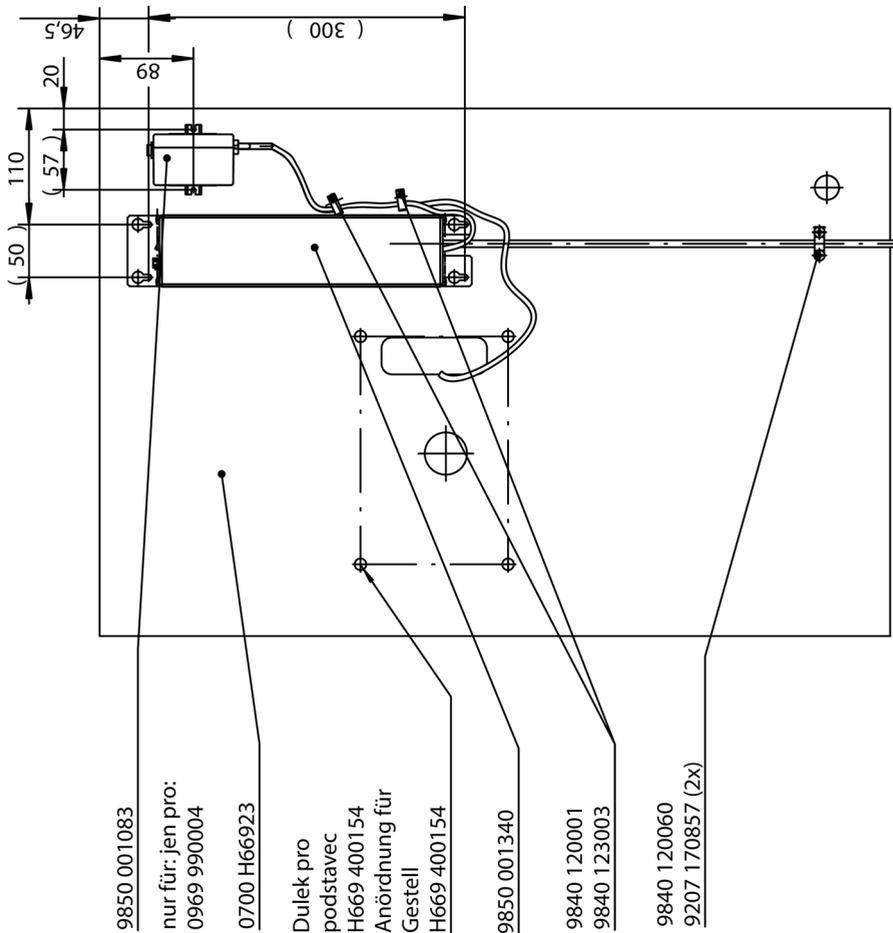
Piano di lavoro fisso, macchine con braccio lungo
